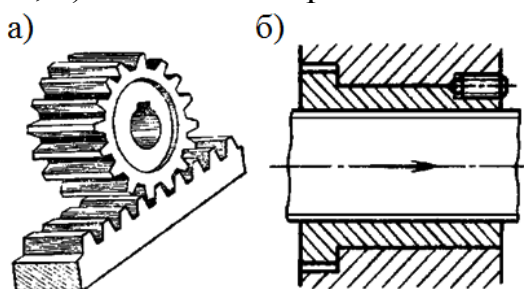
Передачи: а) шестерня – рейка; б) винт – гайка.
